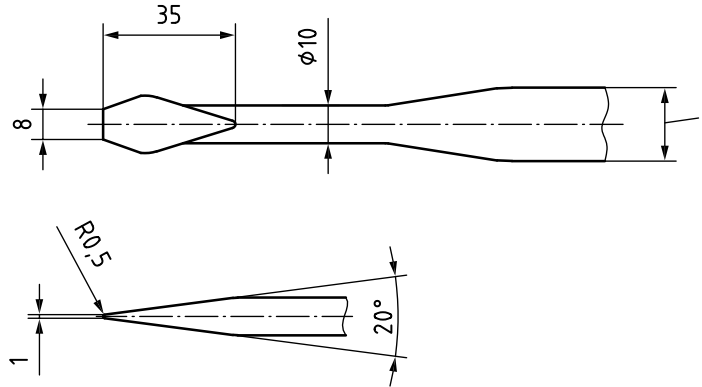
Dimensions typiques des burins pour des essais au burin destructifs
